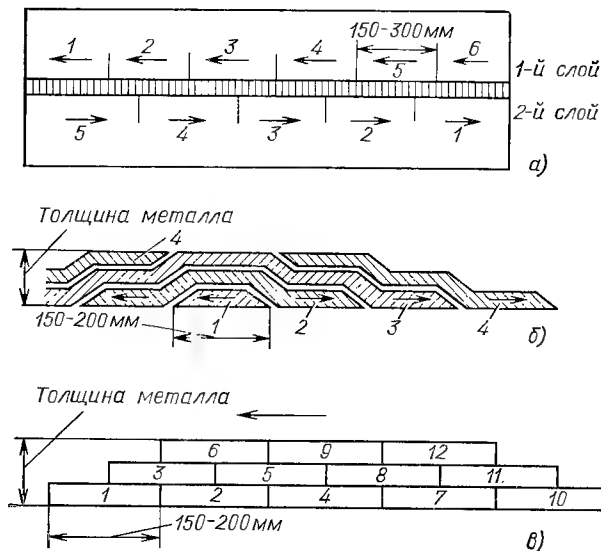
Порядок сварки обратнo-ступенчатым способом (а), «горкой» (б) и «каскадом» (в).
